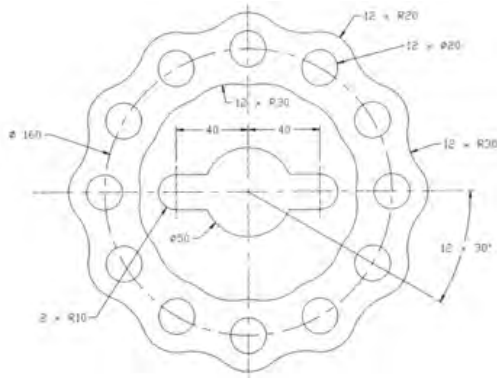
figura construida en MMGS y con un valor de extrusión de 10 milímetros y la pieza se realiza en plano planta.
